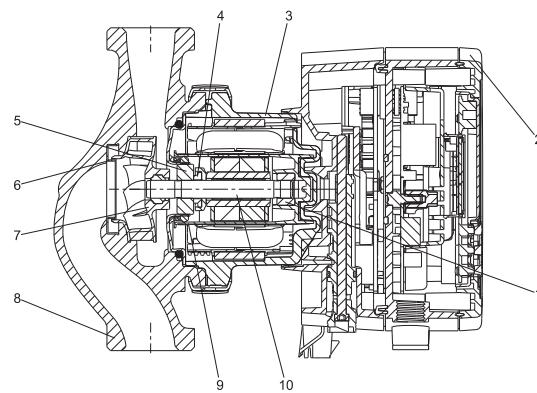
Насос MAGNA3 с корпусом из нержавеющей стали
